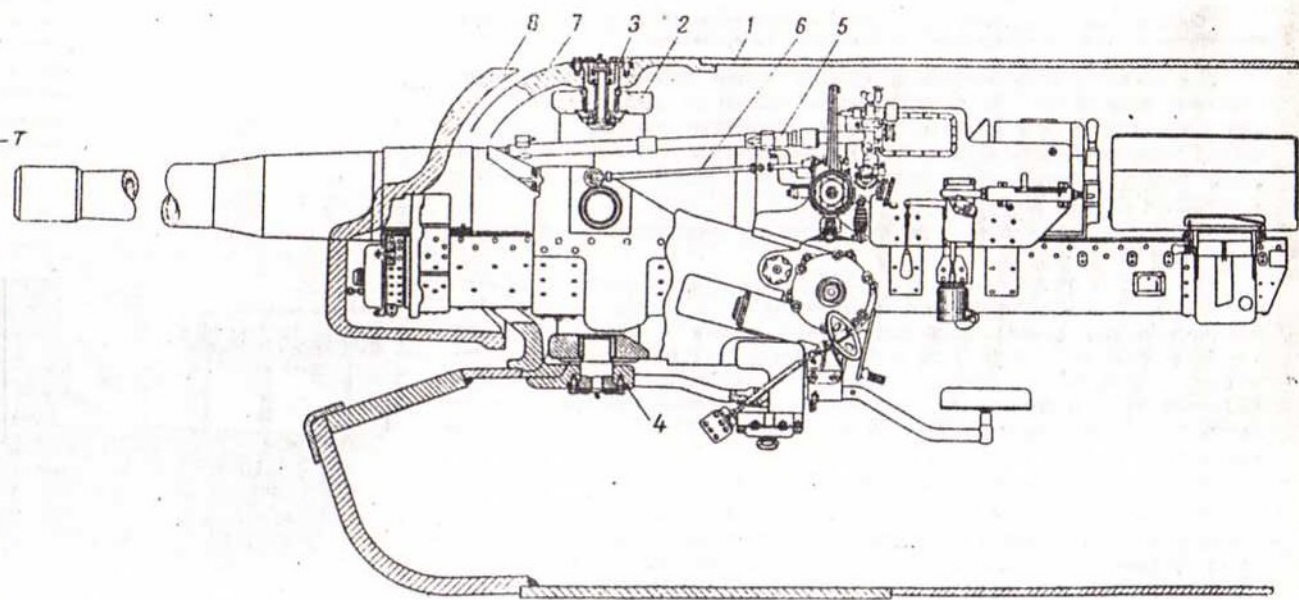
122-мм самоходная пушка обр. 1931/44 г. Общий вид установки орудия в корпусе самоходно-артиллерийской установки (вид слева):
